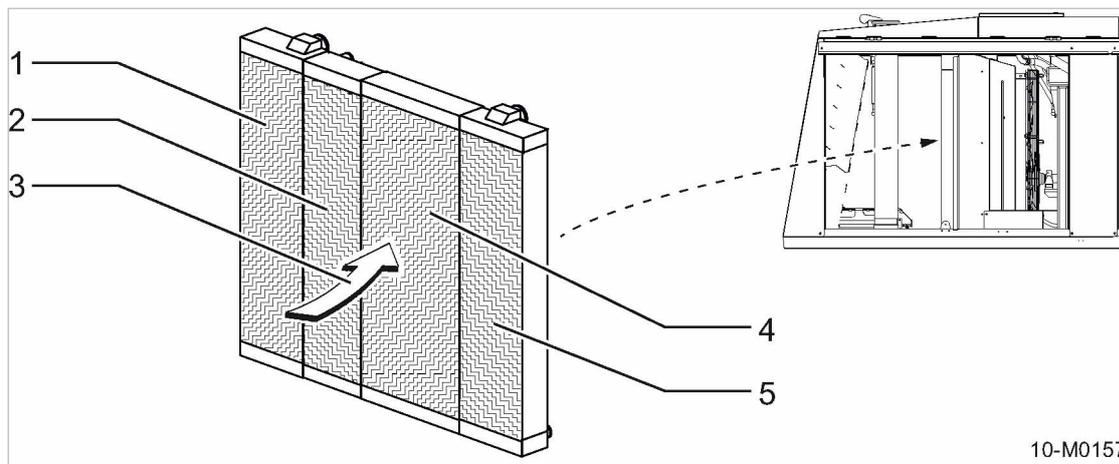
Почистить радиаторы (двигателя и компрессора).
